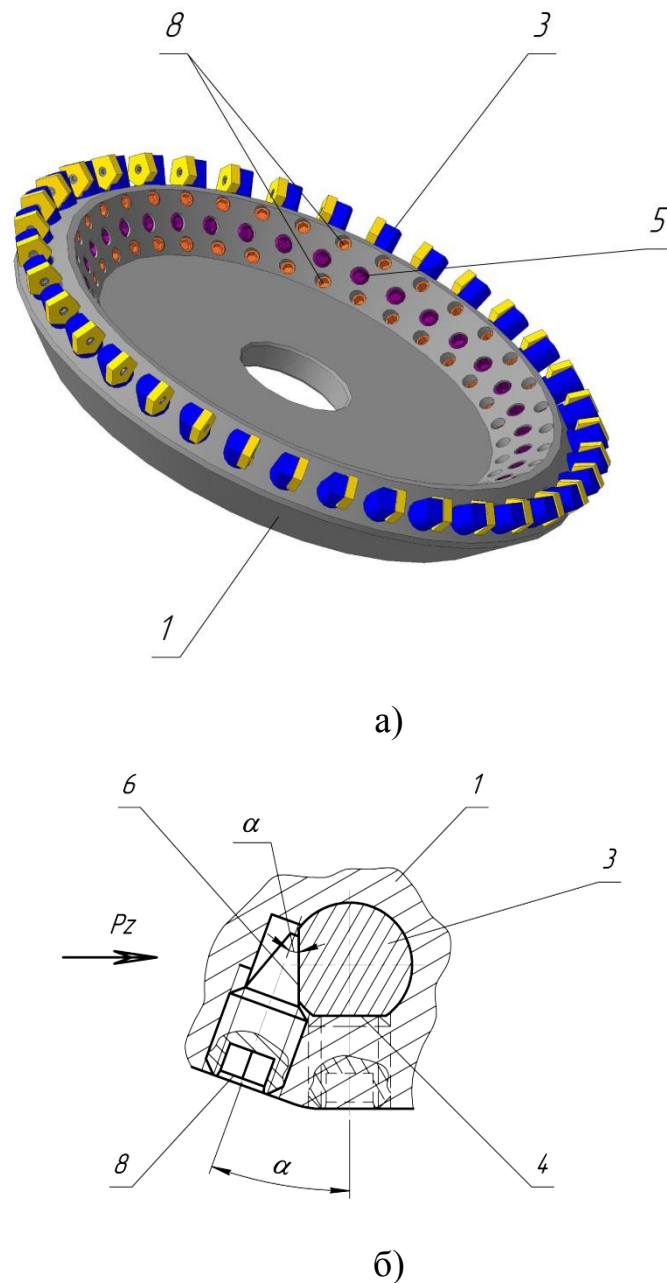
Торцева фреза з п'ятигранними ріжучими пластинами (а)
